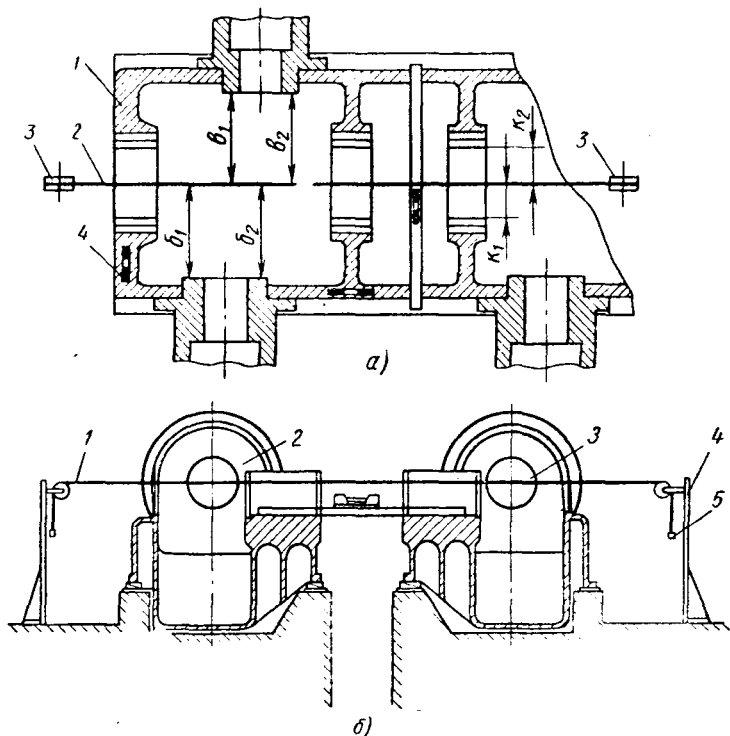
Схема установки центровочных струн в рамах-картерах по оси вала горизонтального компрессора:
